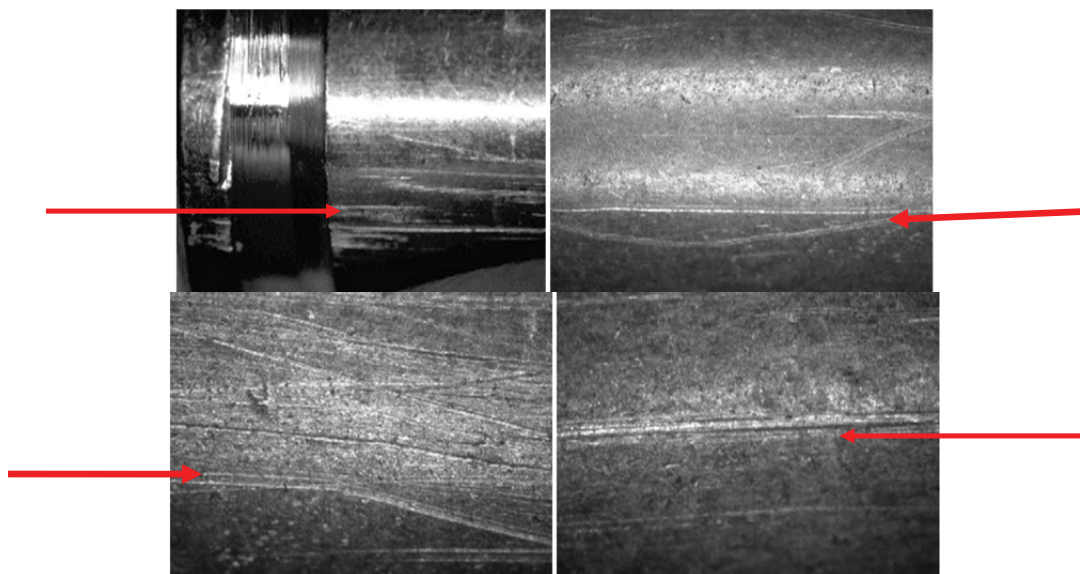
Микрорельеф на корпусе гильз: следы, образованные формовочной матрицей в процессе переснаряжения
